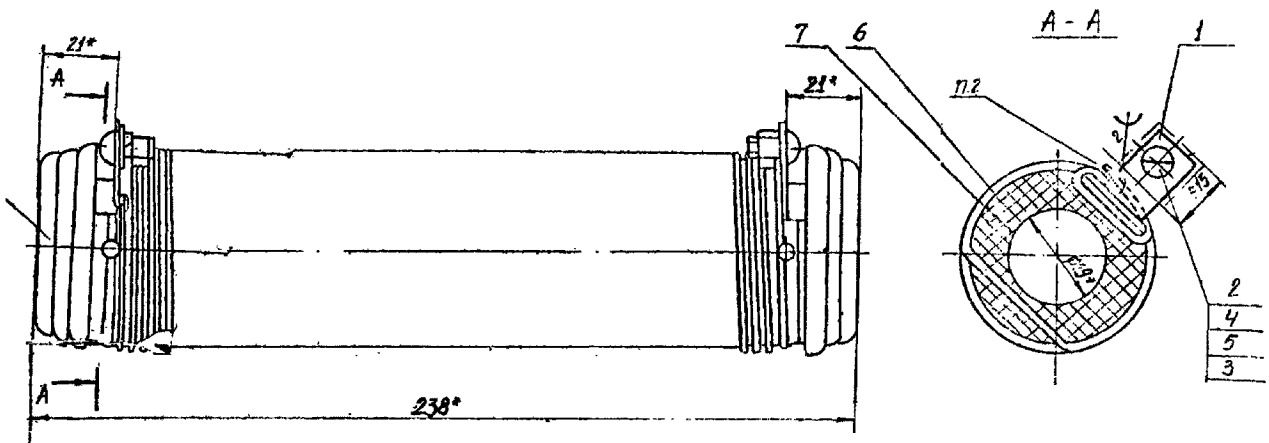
Внешний вид элемента резистора типа СР
